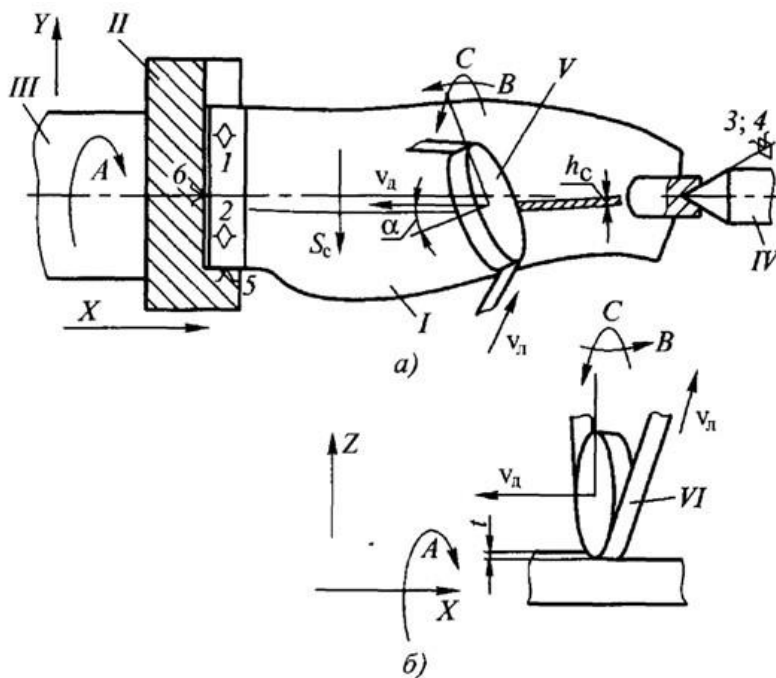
схема базування заготовки й обробки на стрічково-шліфувальному верстаті з ЧПУ: а – схема базування деталі й взаємних переміщень деталі й інструмента при утворенні повздовжнього рядка шириною h_c ; б – схема зняття припуску глибиною t ; α – кут розвороту притискного ролика до напрямку повздовжньої подачі деталі.
